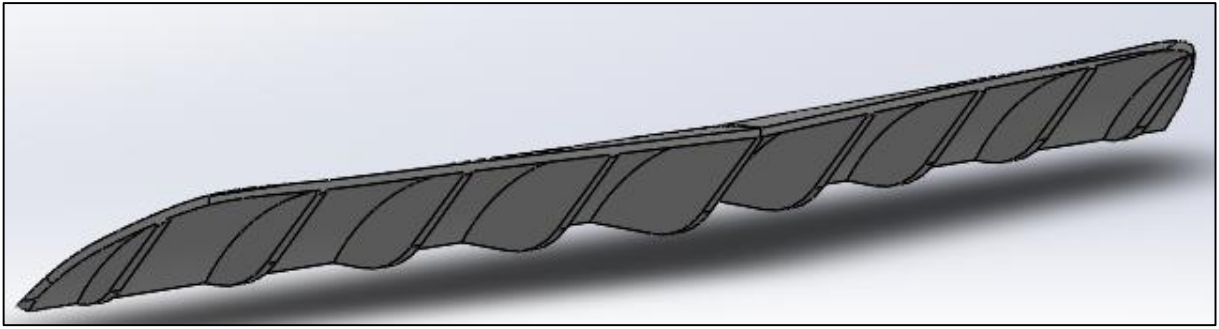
Diseño difusor. Fuente: CAD difusor trasero
